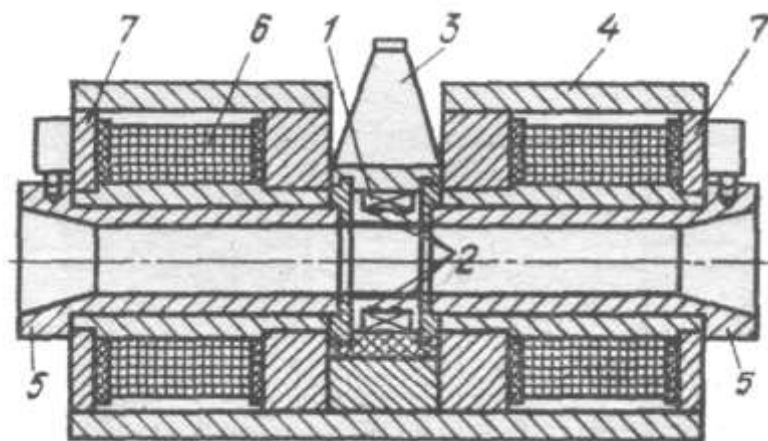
Прохідний вихорострумів перетворювач із змінними навитками: 1 – збуджувальна навитка; 2 – вимірювальні навитки; 3 – блок; 4 – корпус; 5 – змінні вставки; 6 – навитка; 7 – кришки
